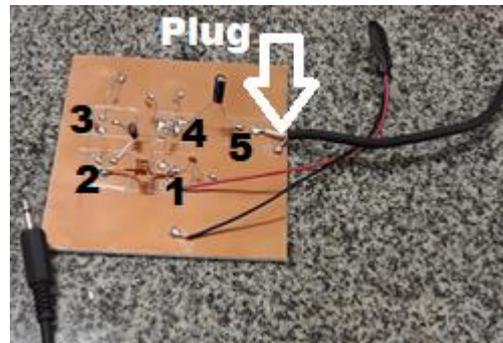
Soldagem do capacitor cerâmico de 10pF e da bobina
